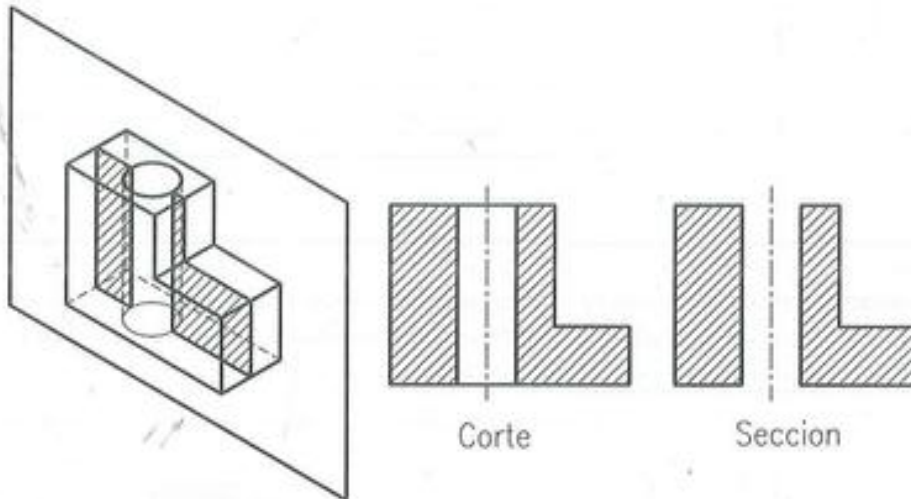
Una pieza cortada por un plano. El resultado puede ser un corte o una sección.
